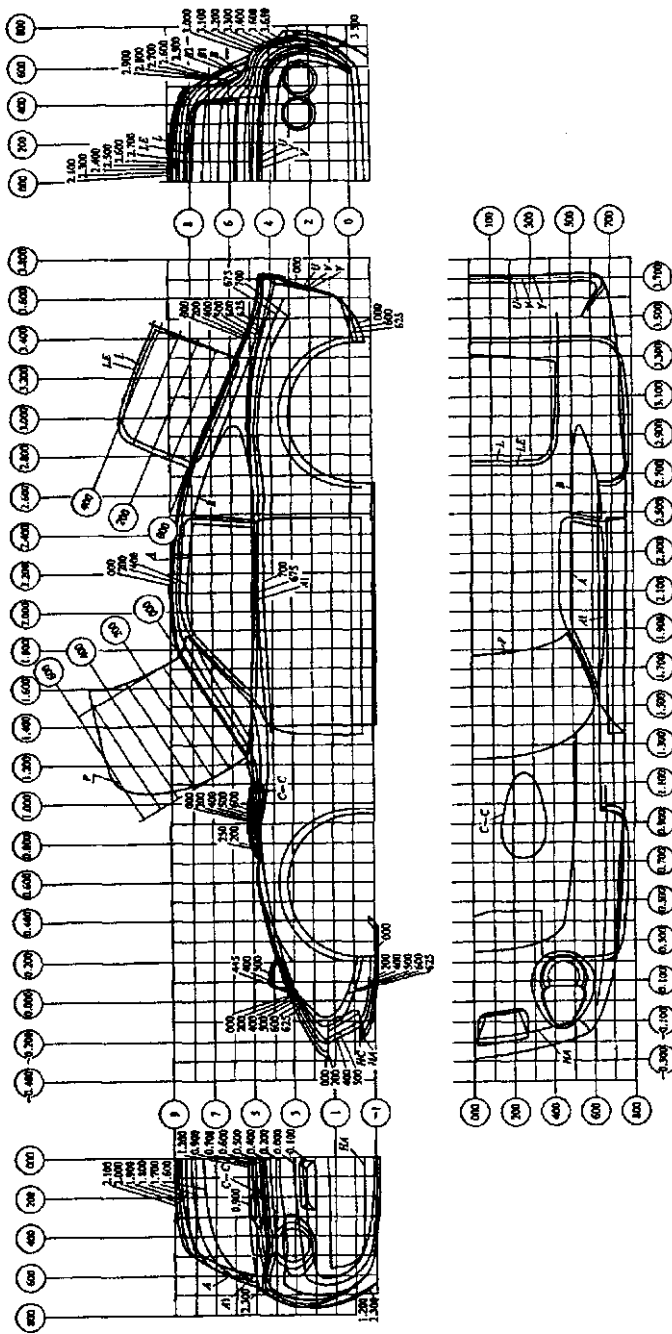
Упрощенный плазовый чертеж поверхности кузова
